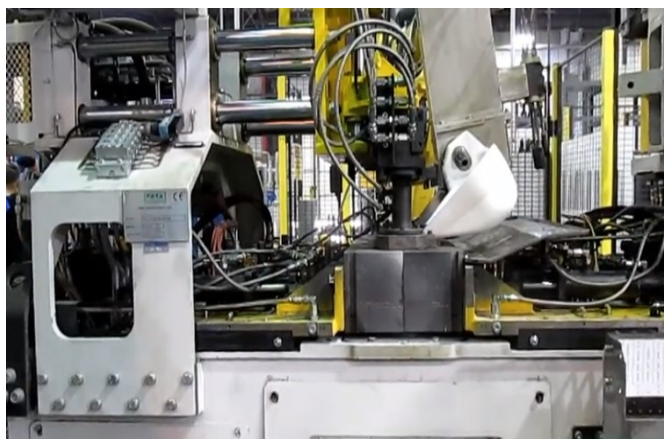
Stroj pro gravitační lití do kovových forem pro výrobu pístů spalovacích motorů firmou FATA – Aluminium piston casting, uprostřed je půlená kovová forma [13]
